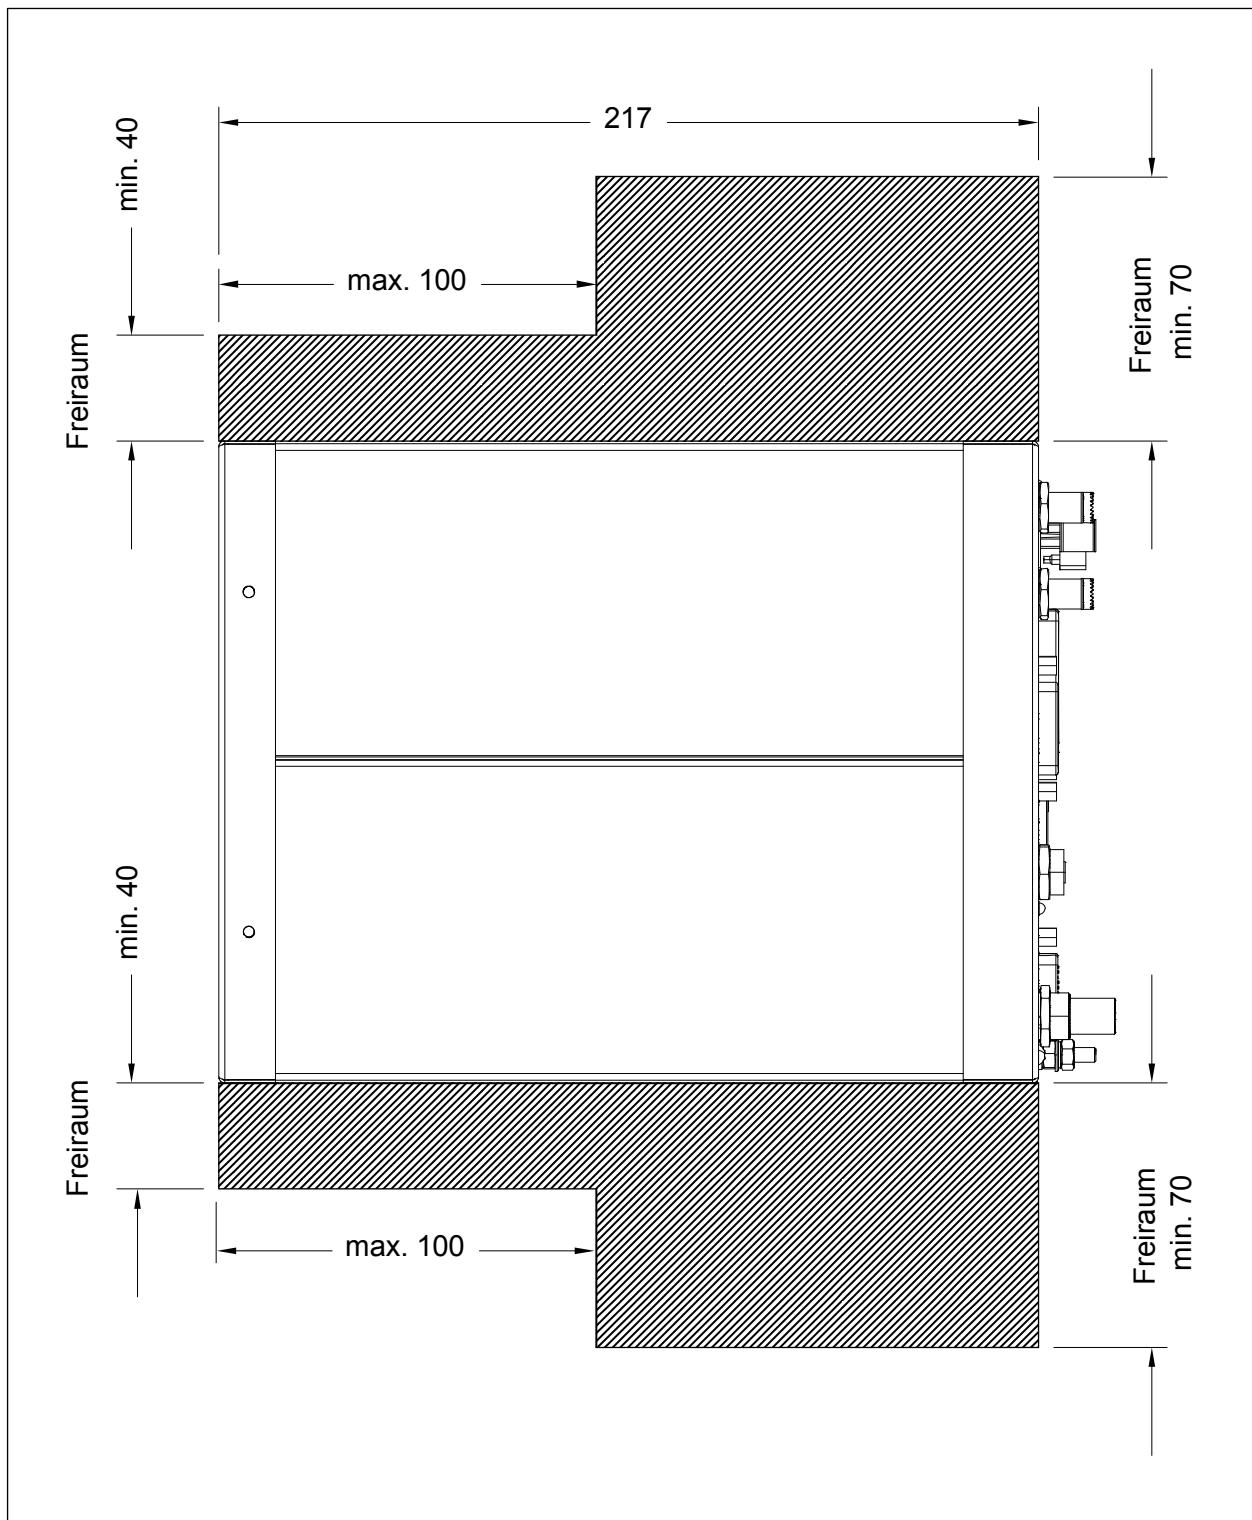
M7002/MA7002 Seitenansicht – Abmessungen in mm
